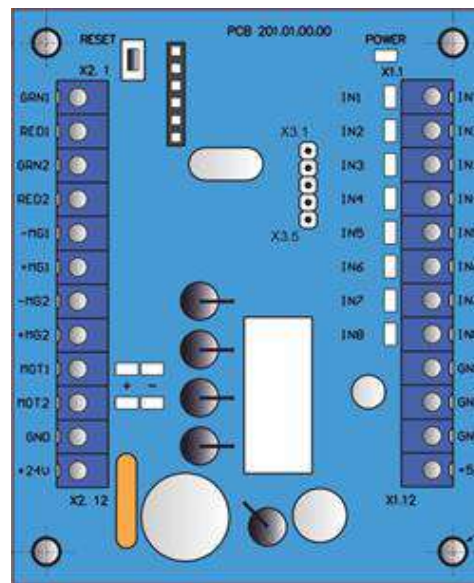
Внешний вид контроллера моторизированного механизма PCB.201.01.00.00
